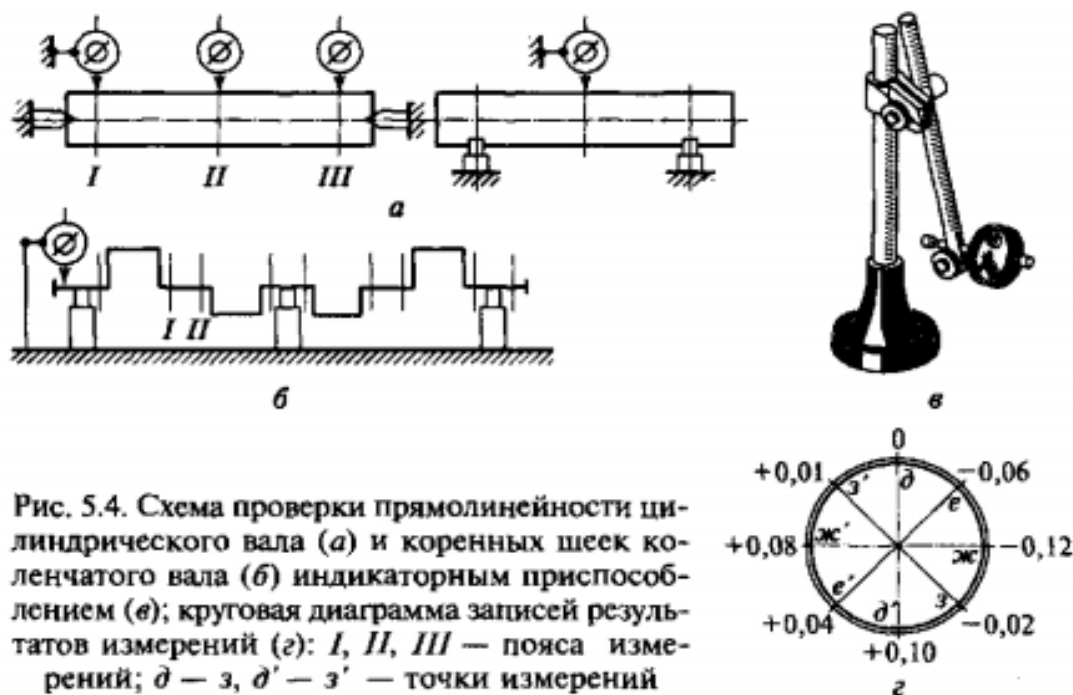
Схема проверки прямолинейности цилиндрического вала (а) и коренных шеек коленчатого вала (б) индикаторным приспособлением (в); круговая диаграмма записей результатов измерений (г): I, II, III — пояса измерений; δ — з, δ' — з' — точки измерений
